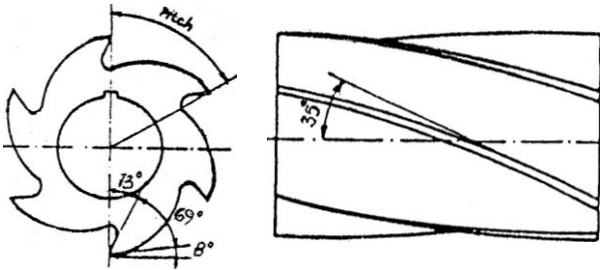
Pisau Frais Mantel (*Plane Milling Cutter*)
